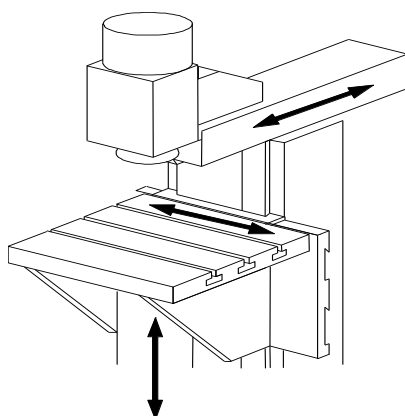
Б. Напрями рухів подач фрезерного верстата з ЧПК
